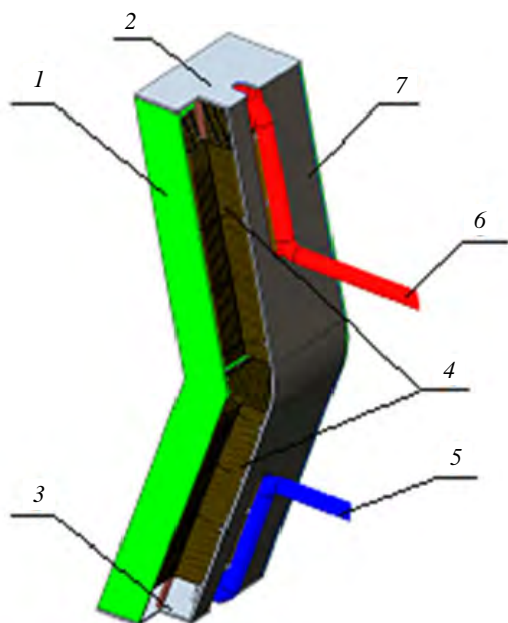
Модуль бланкета: 1 — скоба корпуса; 2 — верхняя крышка корпуса; 3 — нижняя крышка корпуса; 4 — ТВС с твэлами из сырьевого материала; 5 — подводящий патрубков теплоносителя; 6 — отводящий патрубков теплоносителя; 7 — тыльная плита корпуса
